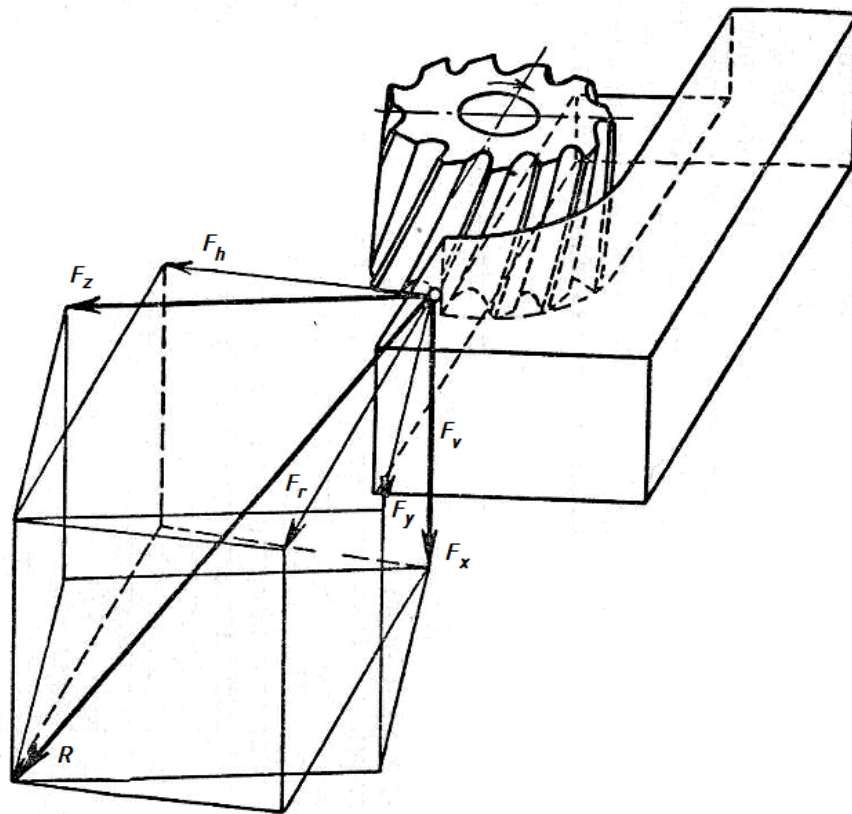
Схема сил різання при торцевому фрезеруванні
